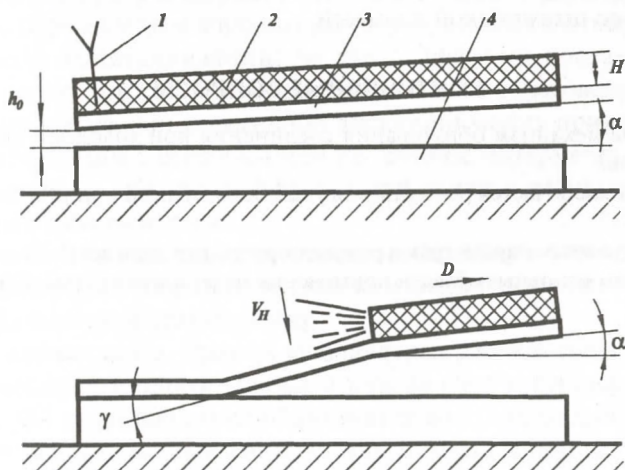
Принципиальная схема сварки взрывом
